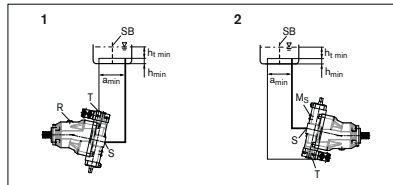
Untertankeinbau mit Einbaulage 1–2
